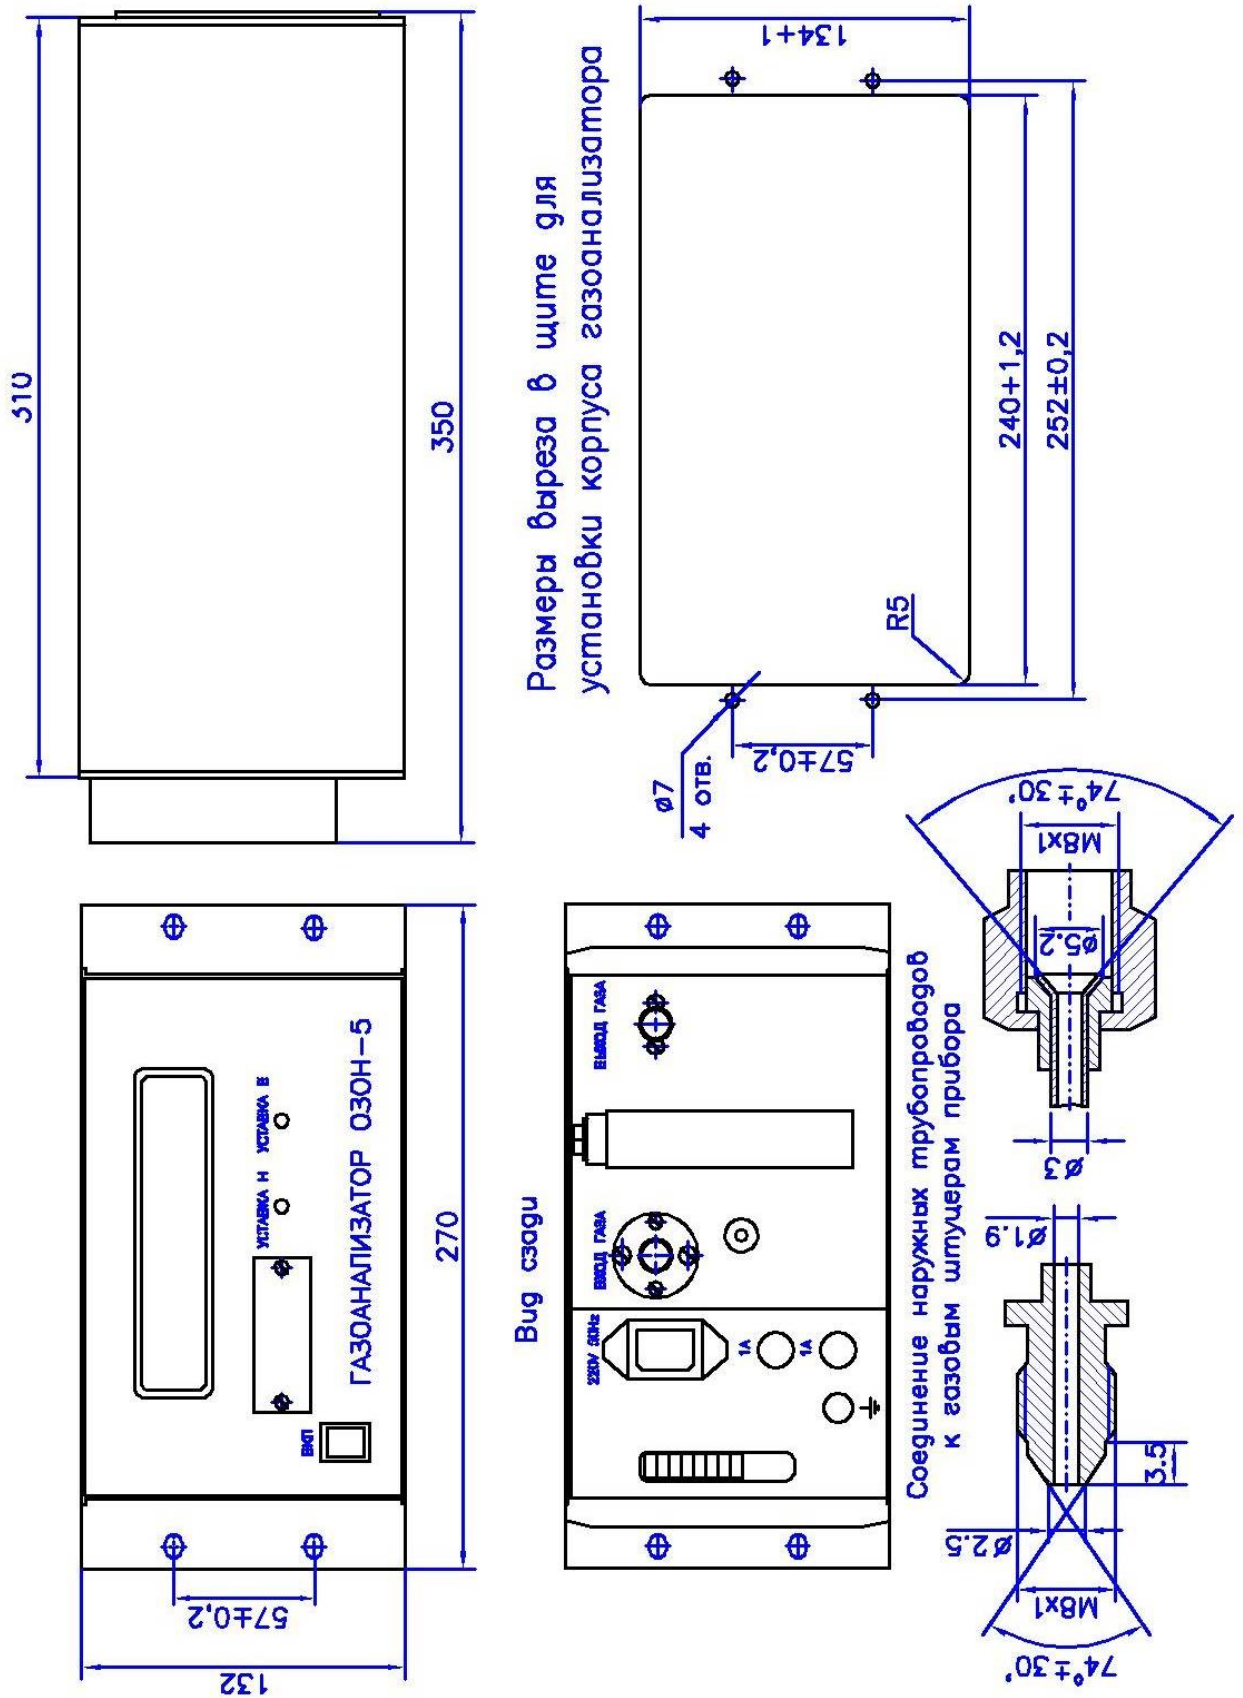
Габаритно-установочный чертеж газоанализатора ОЗОН-5
